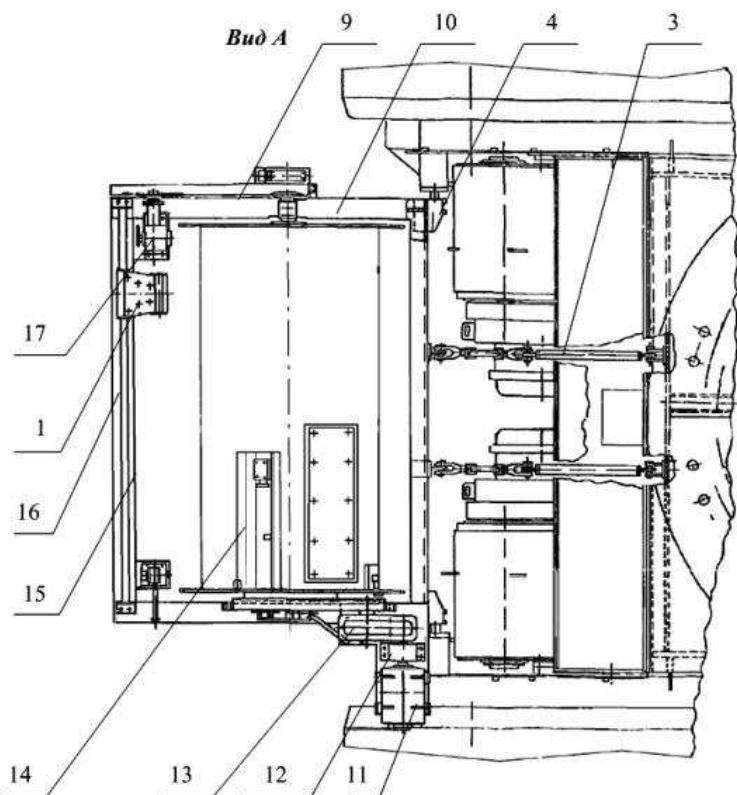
Кабельный барабан (вид сверху)
